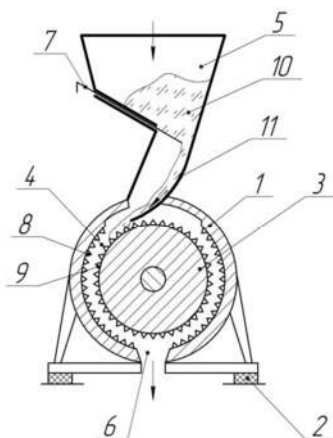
Схема горизонтальной роторной дробилки: 1 - корпус-статор, 2 - амортизирующие прокладки, 3 - ротор, 4 - дробильная камера, 5 - загрузочный бункер, 6 - разгрузочное окно, 7 - заслонка регулировки подачи, 8, 9 - рифли статора и ротора, 10 - исходный продукт, 11 - поверхность наискорейшей подачи
